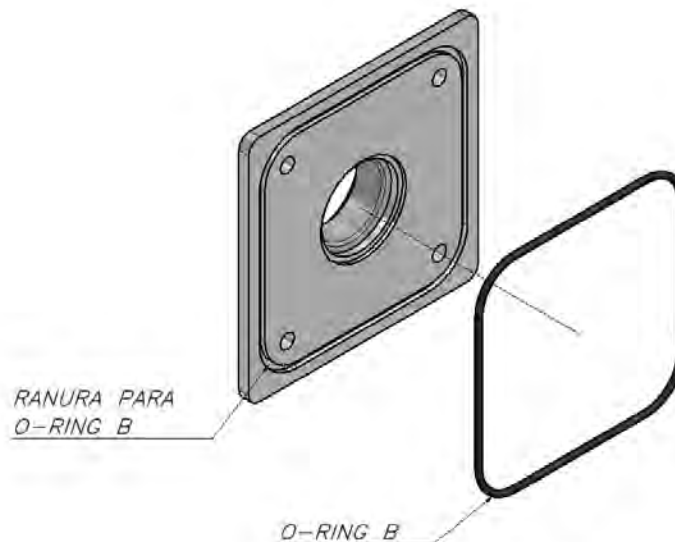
Ensamble del sellado estático para el soporte de rodamiento
